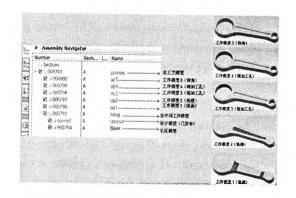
连杆制造工序模型实例 Fig. 7 Example of manufacturing process of connecting rod
